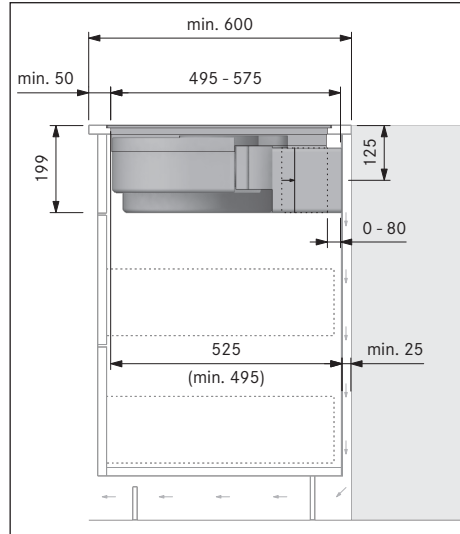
Monteringsdimensjoner ved resirkulering, monteringsvariant A
